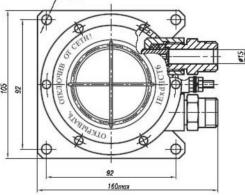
Габаритный чертёж светового Оповещателя ExOППС-1B-CM в алюминиевом корпусе
